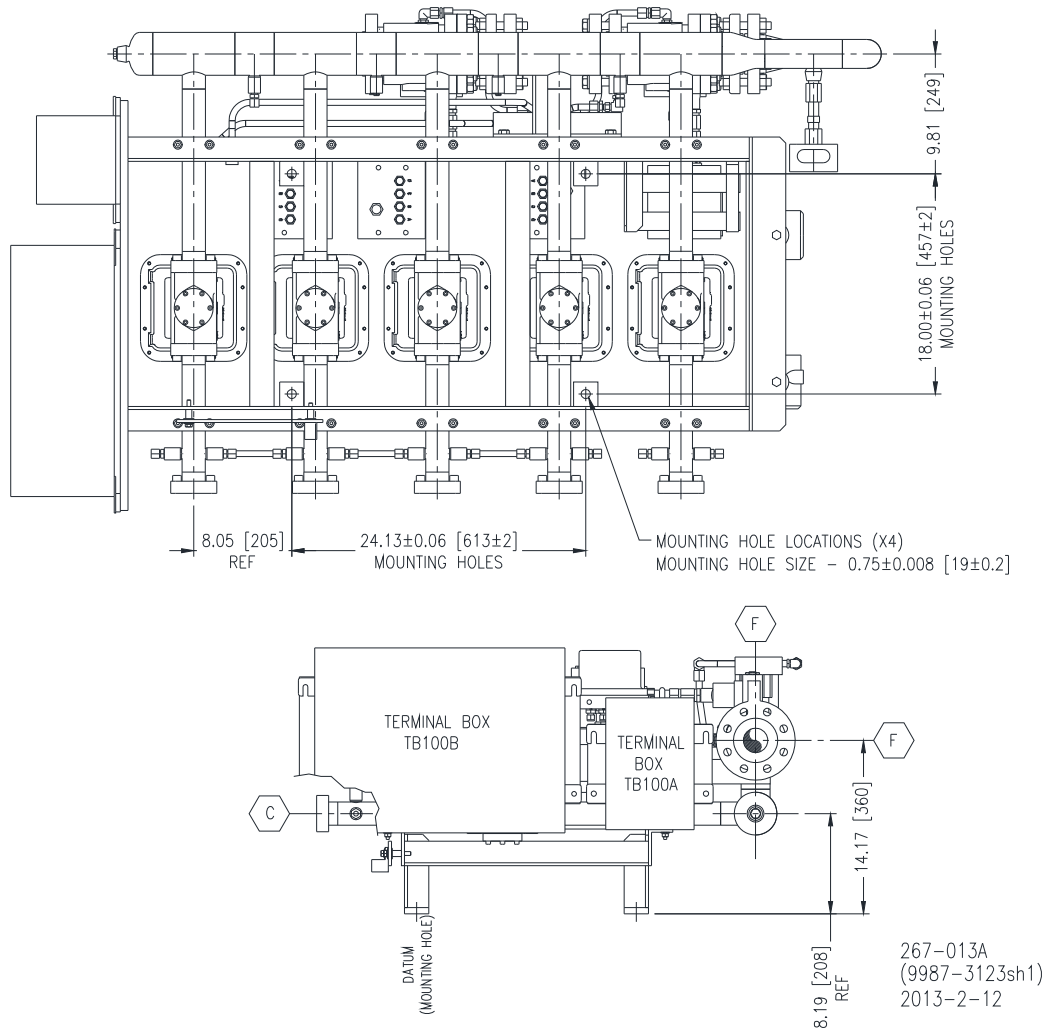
Módulo de Combustível Woodward PGT25+ G4 DLE e LM2500+ G4 DLE com GS6 padrão
